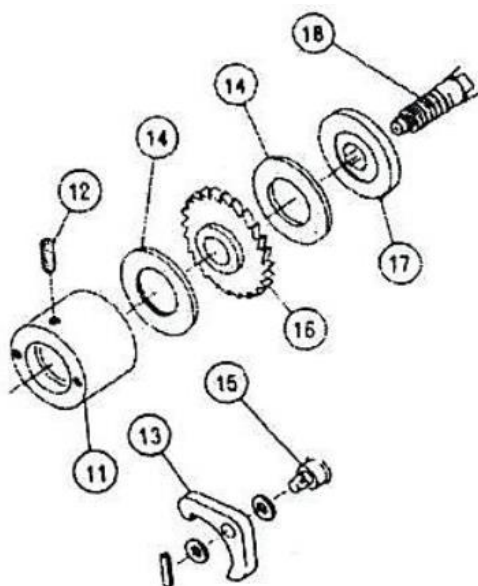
Схема установки тормозных фрикционных дисков лебедки ручной GEARSEN JHW (11 - контргайка, 12 - винт, 13 - захват храповика, 14 - фрикционная пластина, 15 – ось храповика, 16 – храповик в сборе, 17 – пружинное стопорное кольцо, 18 - вал)
